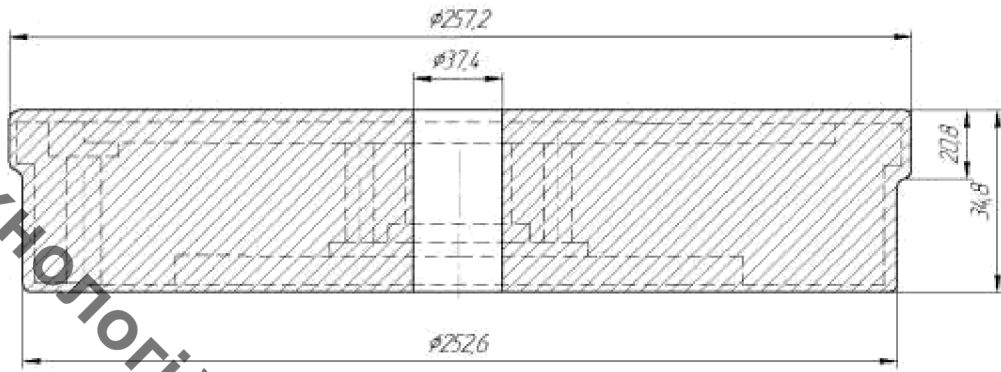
Ескіз заготовки в піщано-глинисті форми
